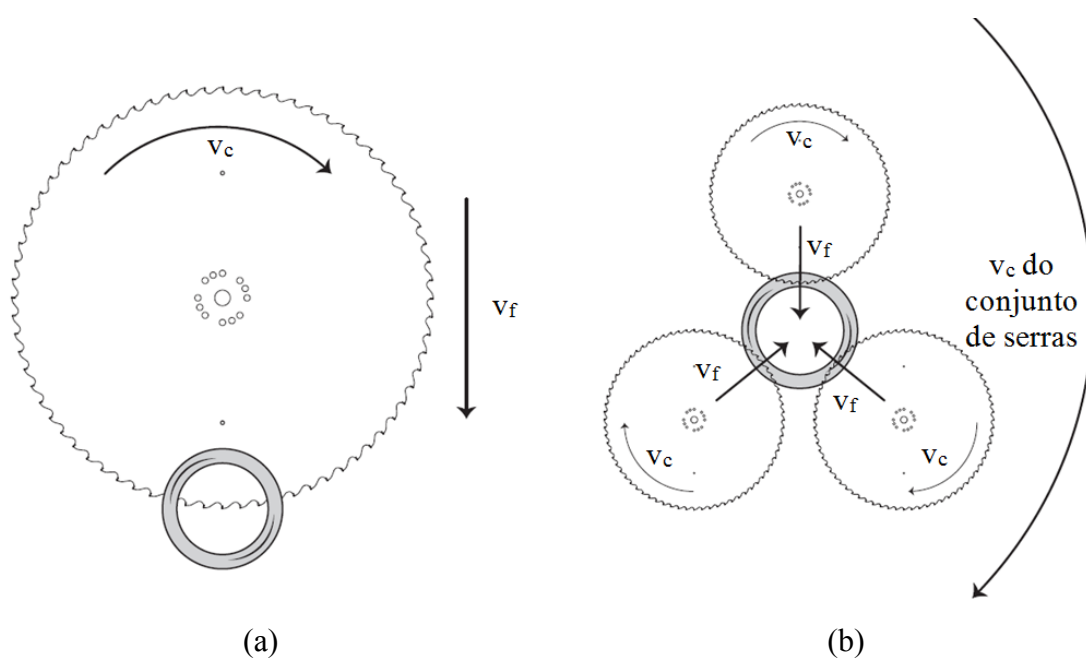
Serramento circular de tubos com: (a) serra convencional e (b) várias serras
